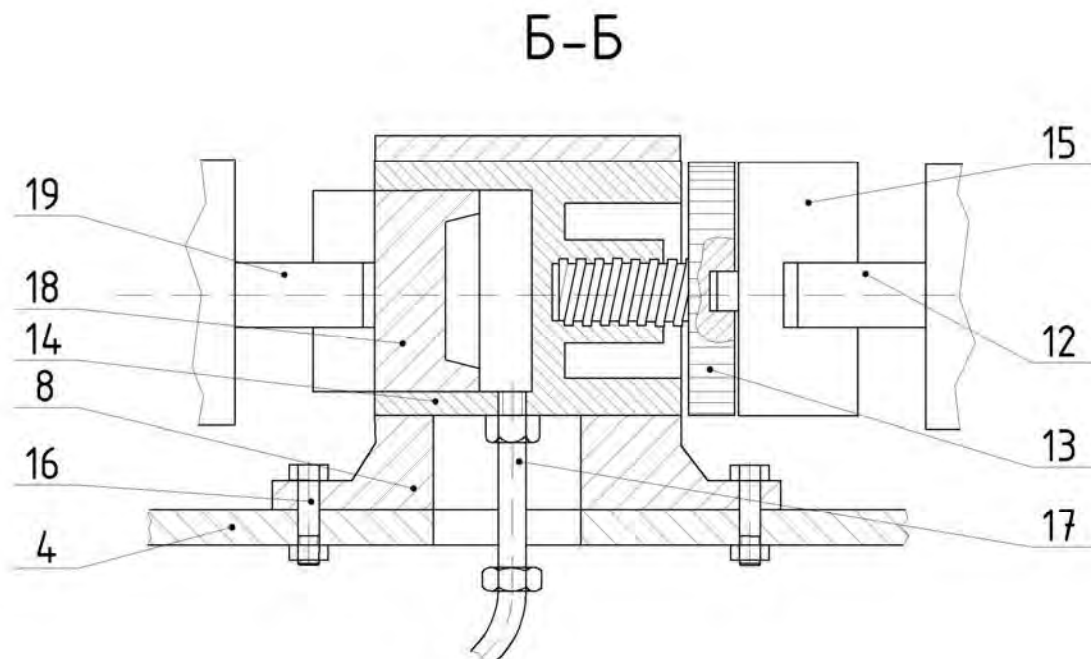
Разрез гидравлического цилиндра тормоза ведущего переднего моста колесного трактора с двумя первичными тормозными колодками: 4 – тормозной щит; 8 – корпус; 12 – тормозная колодка; 13 – винт регулировочный; 14 – гидроцилиндр; 15 – опора; 18 – поршень; 19 – тормозная колодка
